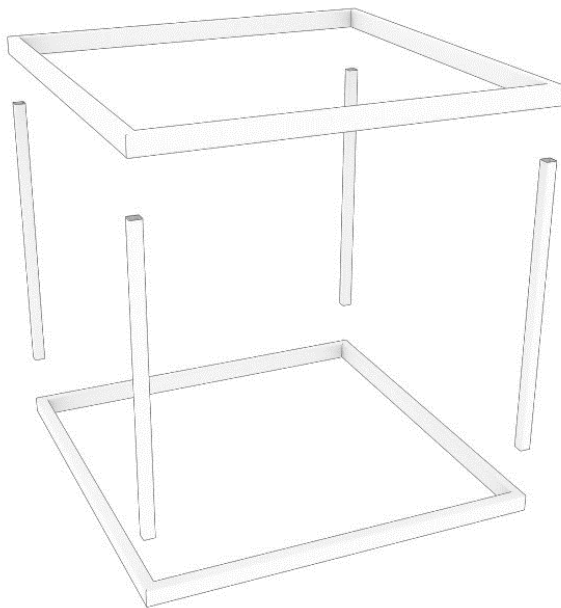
EXPLOSIONADO DEL ESQUELETO. FUENTE PROPIA
